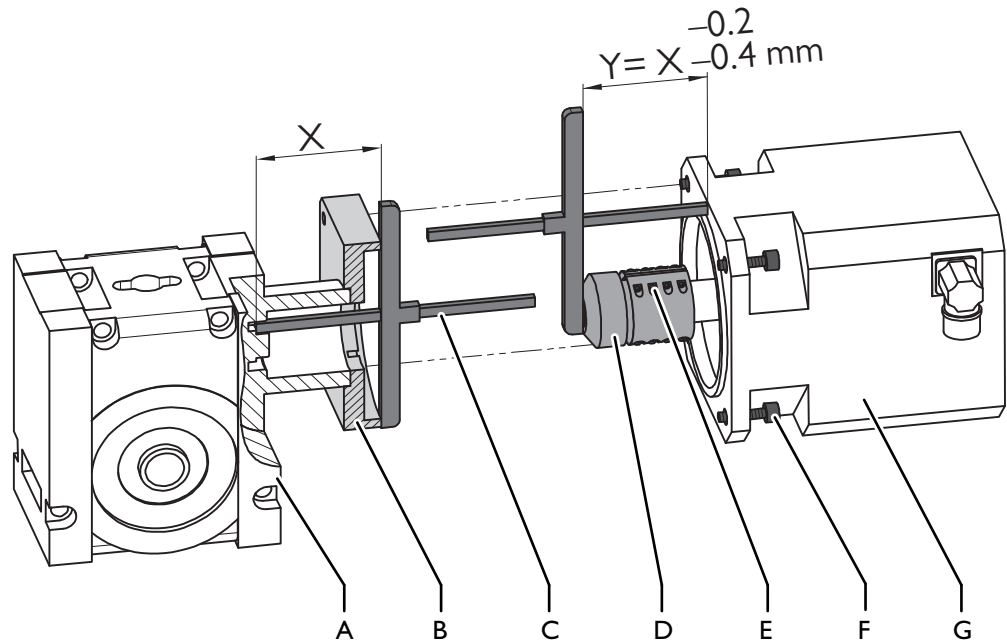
Posicionar el acoplamiento sobre el eje del motor
